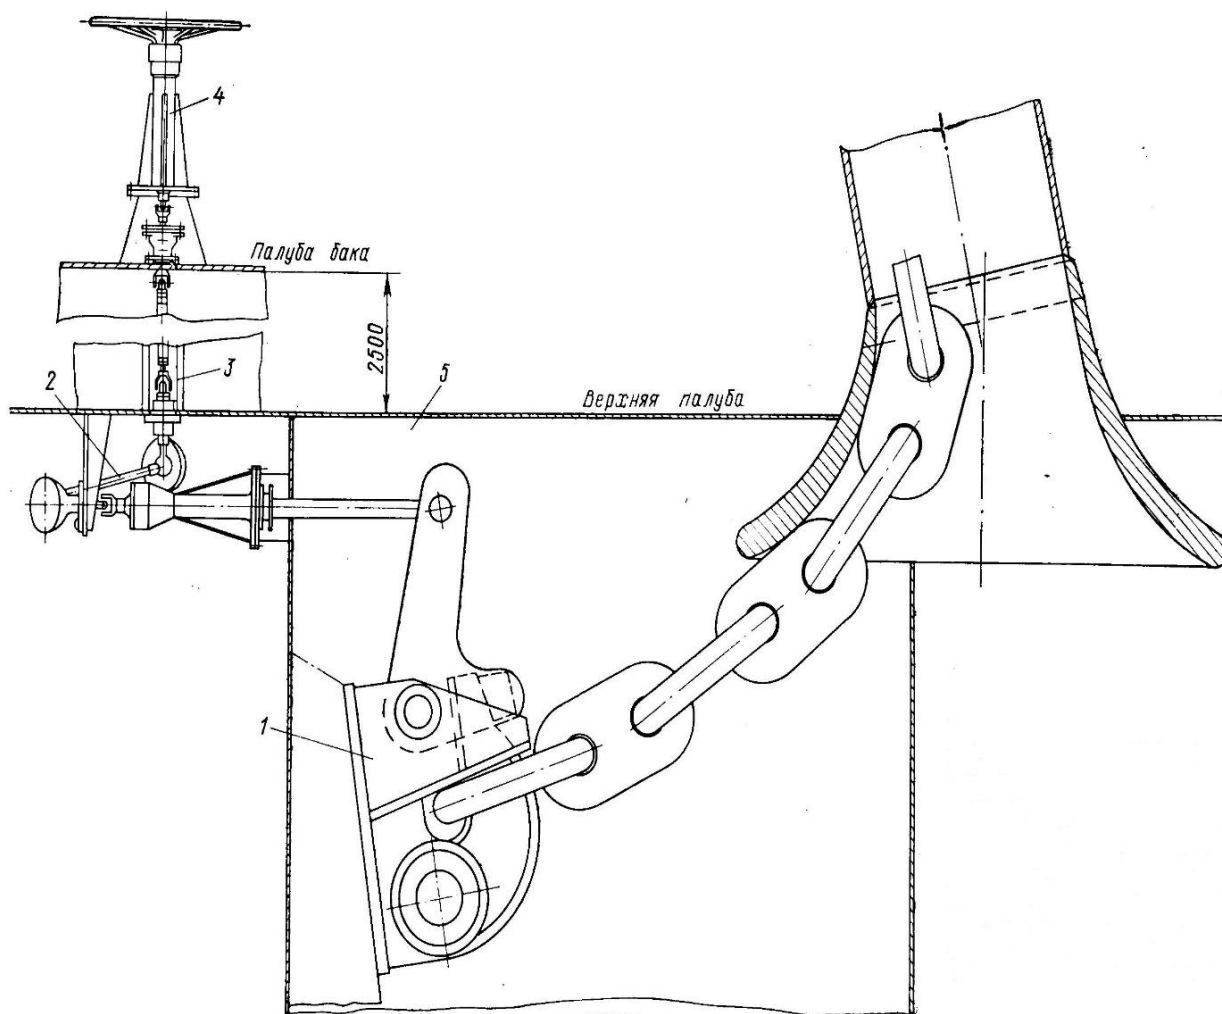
Устройство для крепления и отдачи коренного конца
